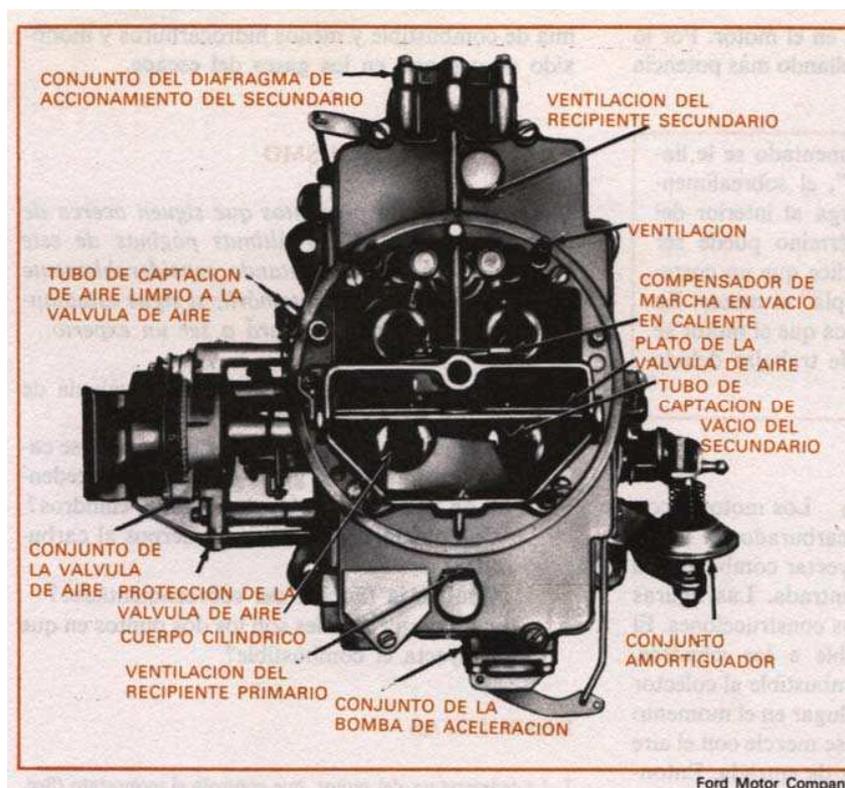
Vista superior de un carburador cuádruple, o de cuatro cuerpos.
